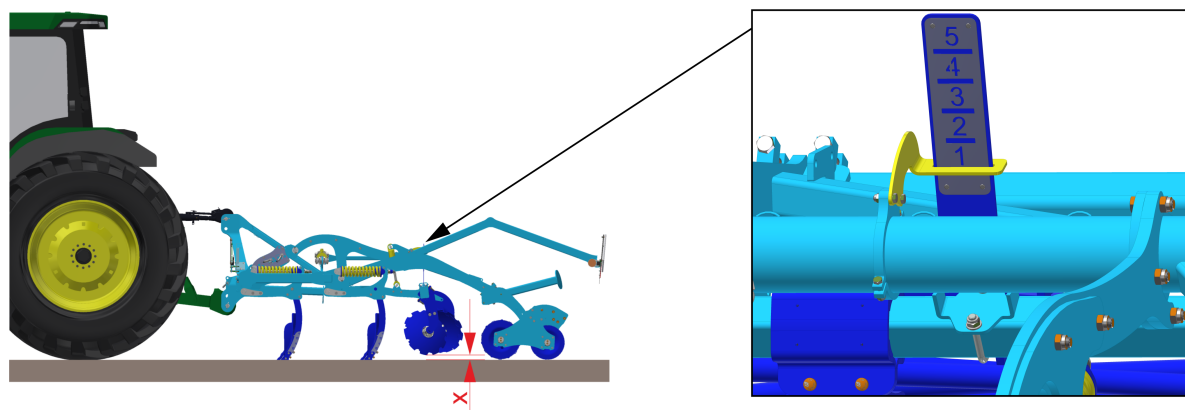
Disques de nivellement latéraux réglables en hauteur
